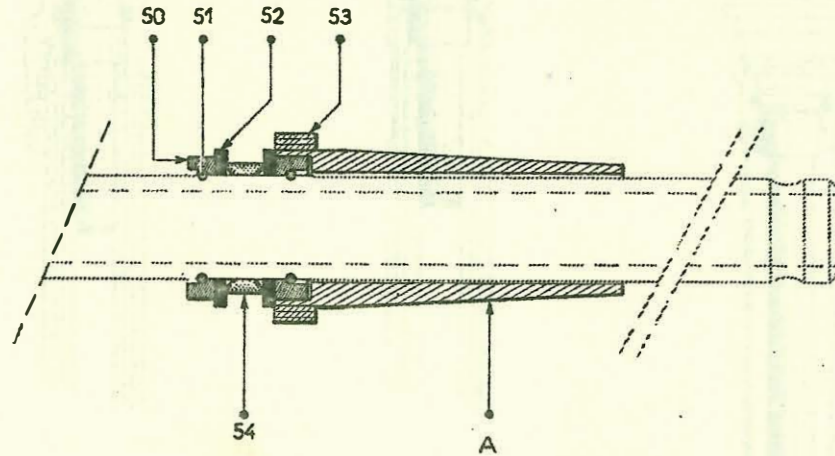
Einbau des Rilsanrings 32 für Zylinderendstück
